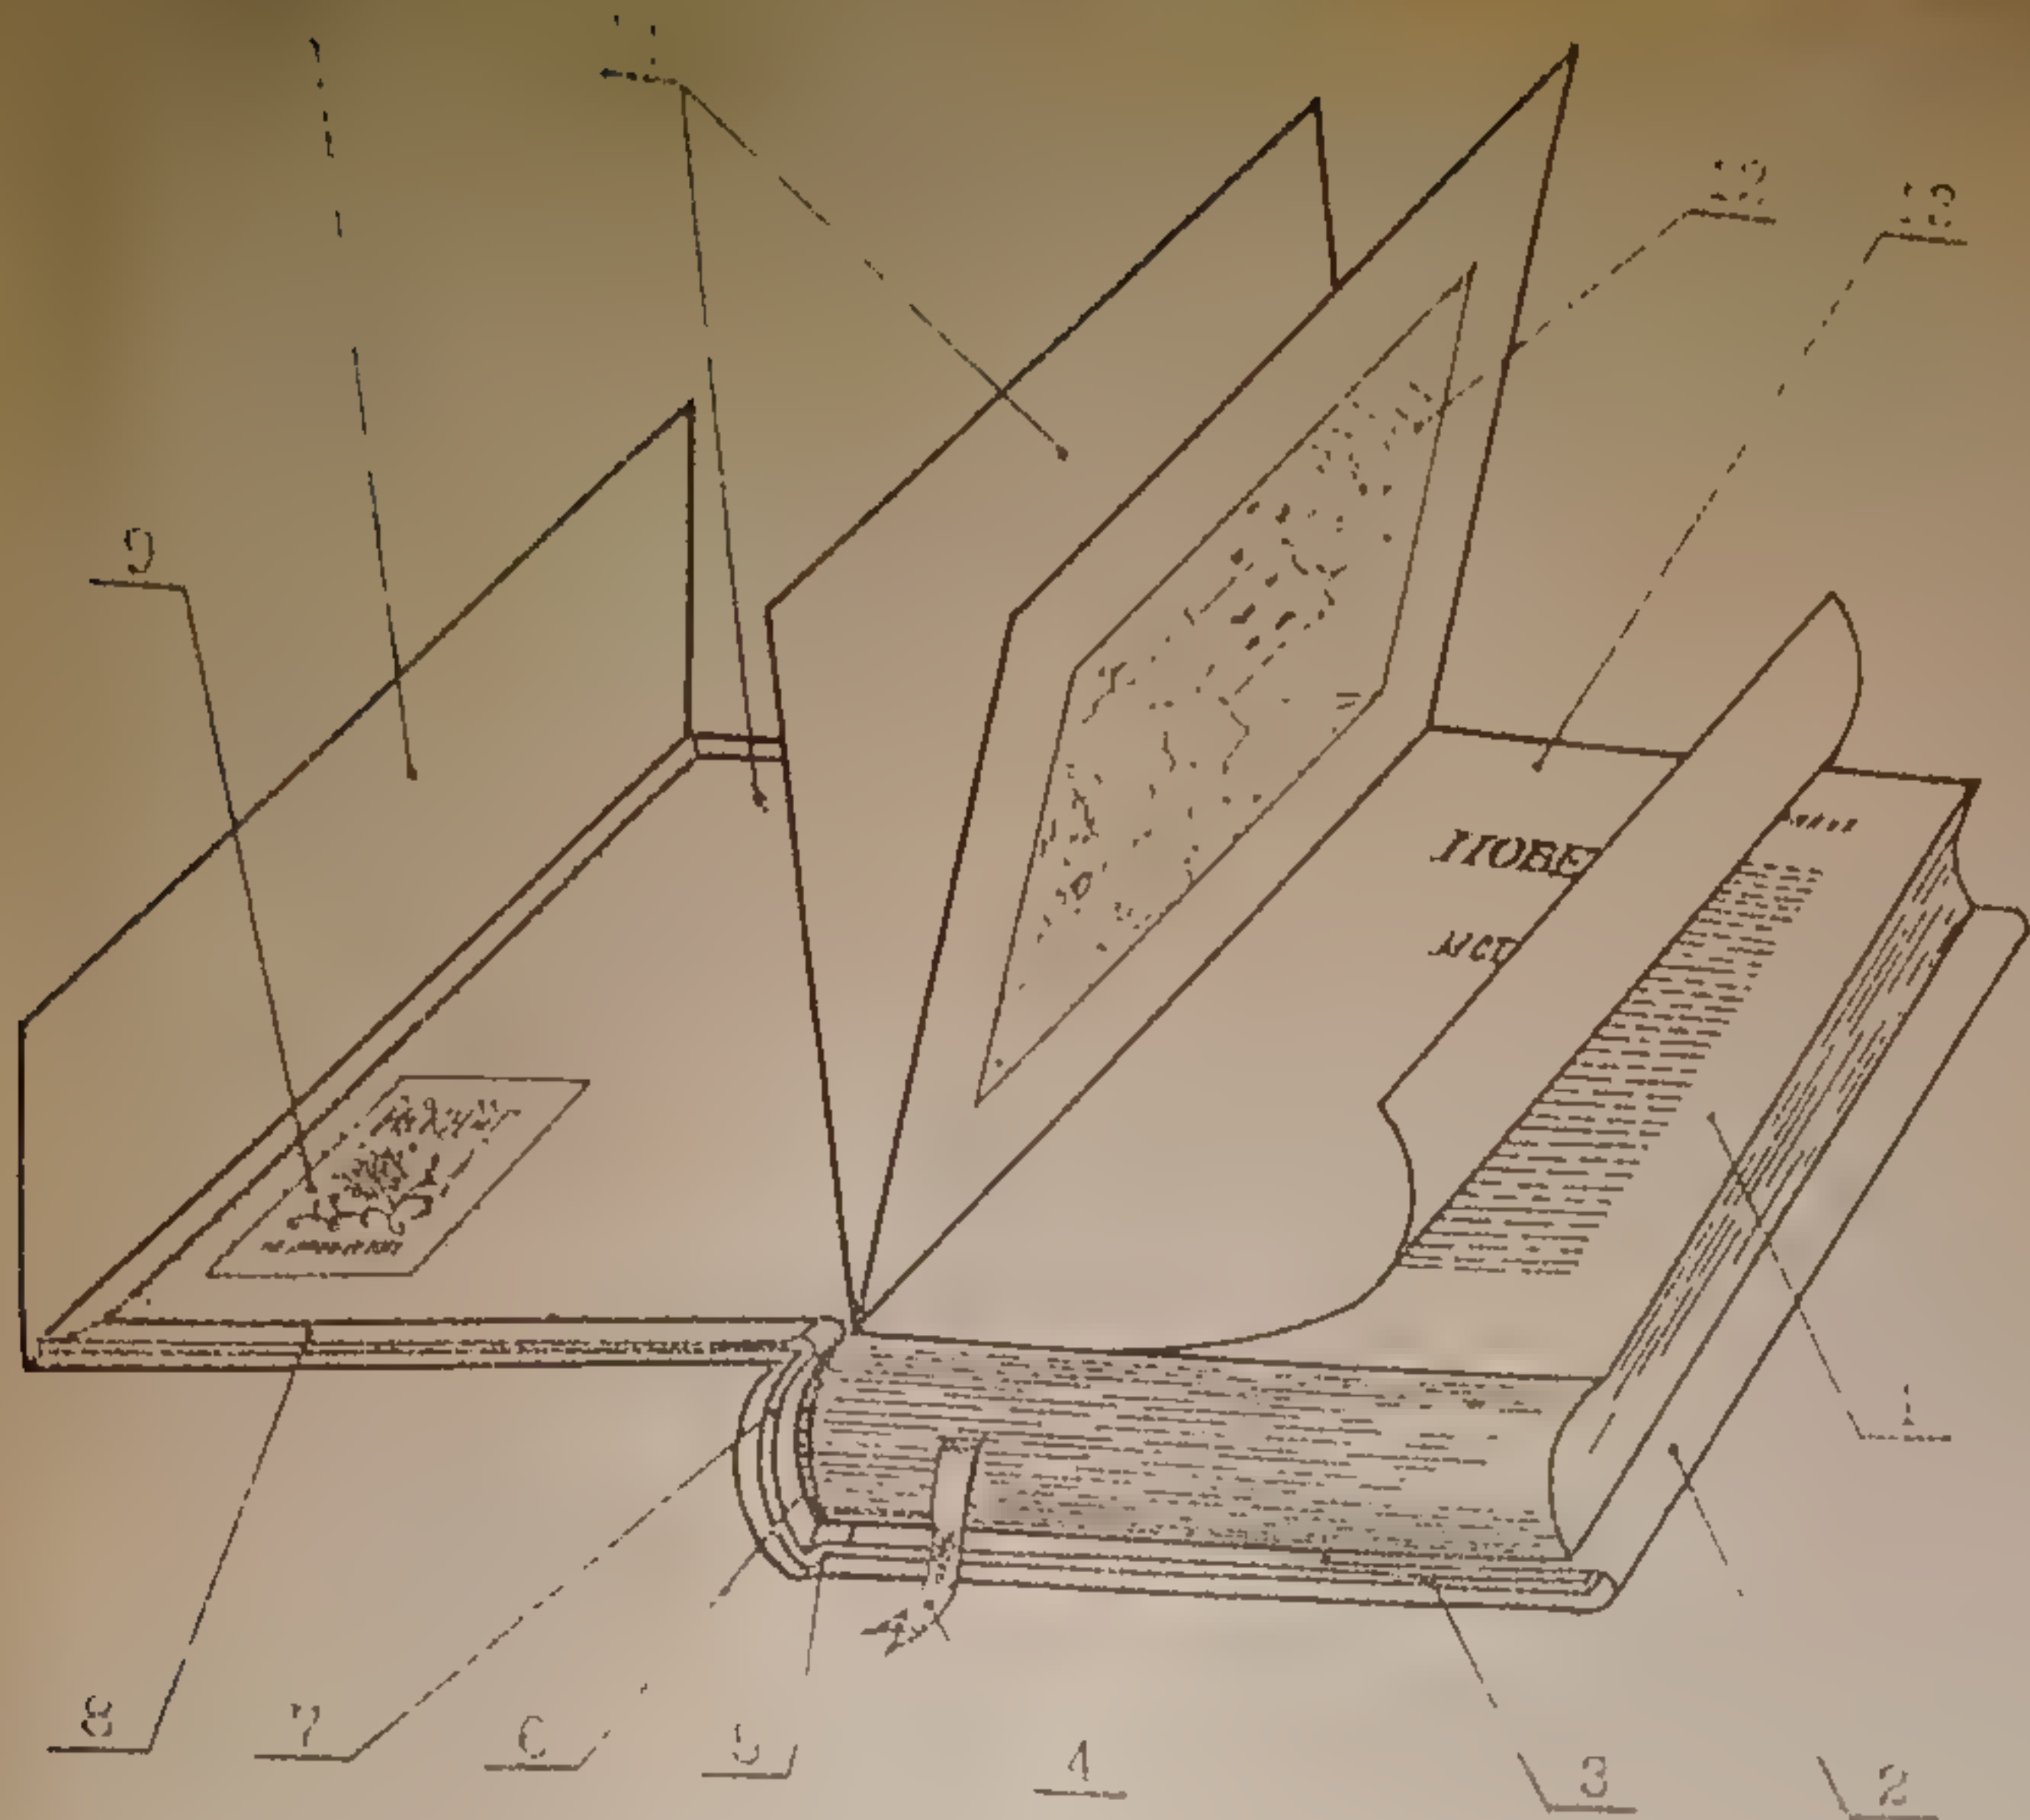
Книга: 1 — книжный блок; 2 — суперобложка; 3 — переплетная крышка; 4 — ляссе; 5 — рубчик; 6 — каптал; 7 — корешок; 8 — кант; 9 — эксlibрис; 10 — клапан суперобложки; 11 — форзац; 12 — фронтиспис; 13 — титульный лист
